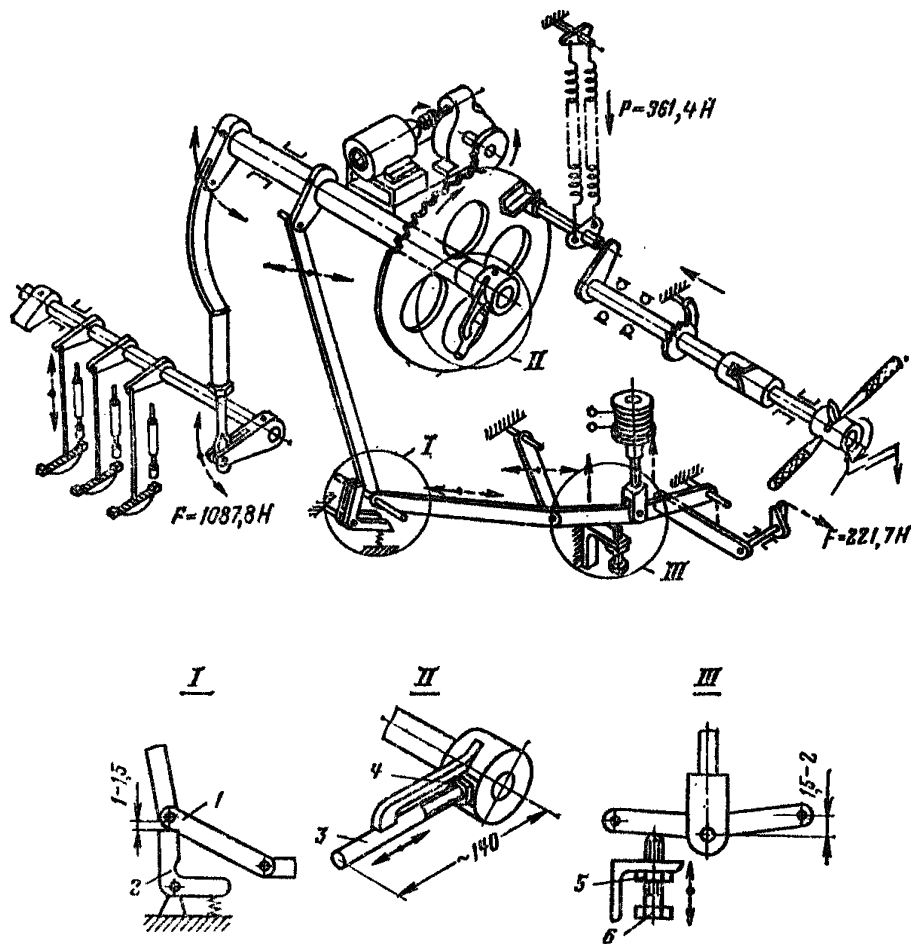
Кинематическая схема встроенного пружинного привода ячейки РВД-6
